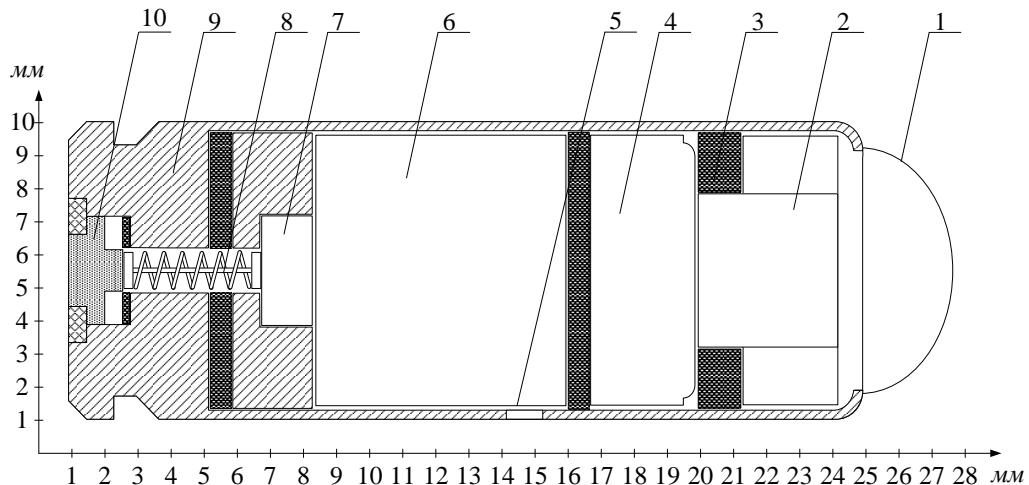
Конструкція модуля «Лазерний випромінювач»: 1 – збірка лінз; 2 – лазерний діод; 3 – корпусні фіксатори; 4 – елементи живлення; 5 – вікно налаштування; 6 – електронна схема; 7 – мікроперемикач; 8 – пружина; 9 – корпус гільзи; 10 – ударна пластинка
